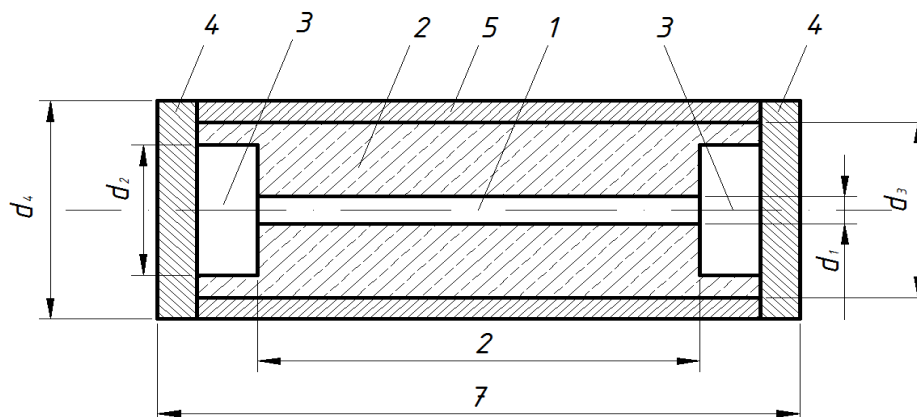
Модель жидкометаллического самовосстанавливающегося предохранителя
